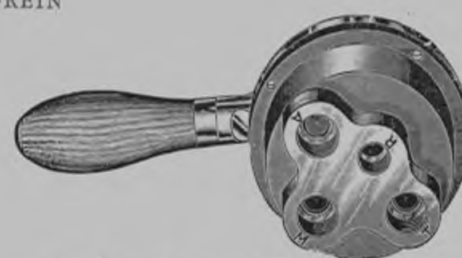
ROBINET DE MANŒUVRE (VUE EN DESSOUS)
